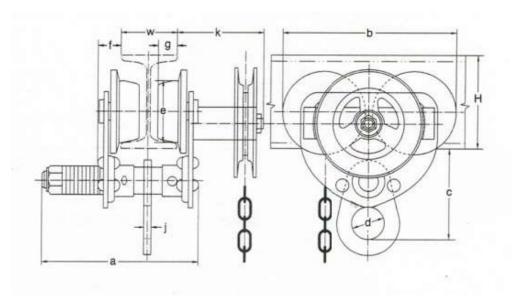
Габаритные размеры тележки приводной для тали тип В.
